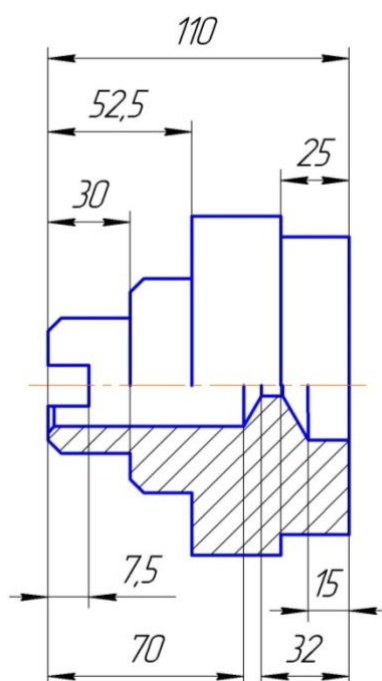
Чертеж детали с линейными размерами, проставленными от баз
